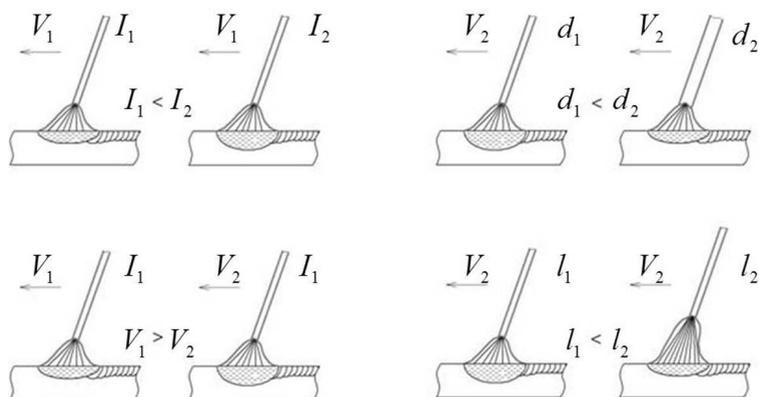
Факторы, определяющие глубину проплавления основного металла при сварке
